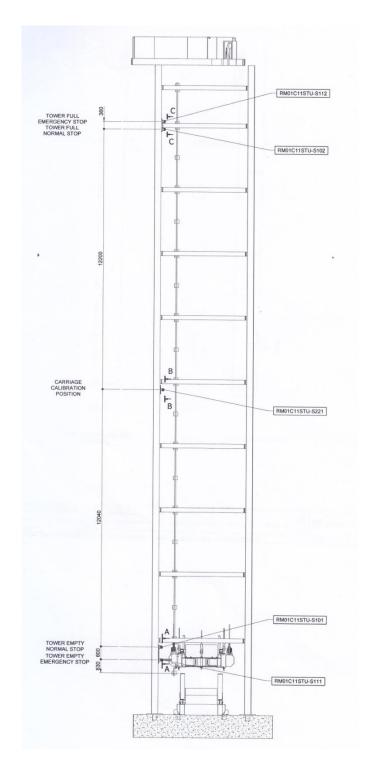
Установка магнитных переключателей на металлической конструкции вертикального накопителя
